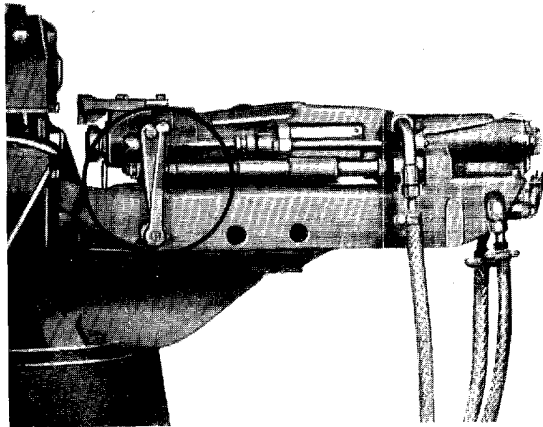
Maschine mit angebaute Lochhammer und Schalterhebel für diesen
